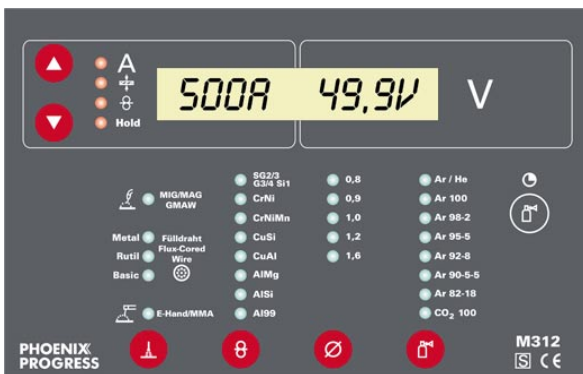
Display des Schweißgerätes PHOENIX PROGRESS
